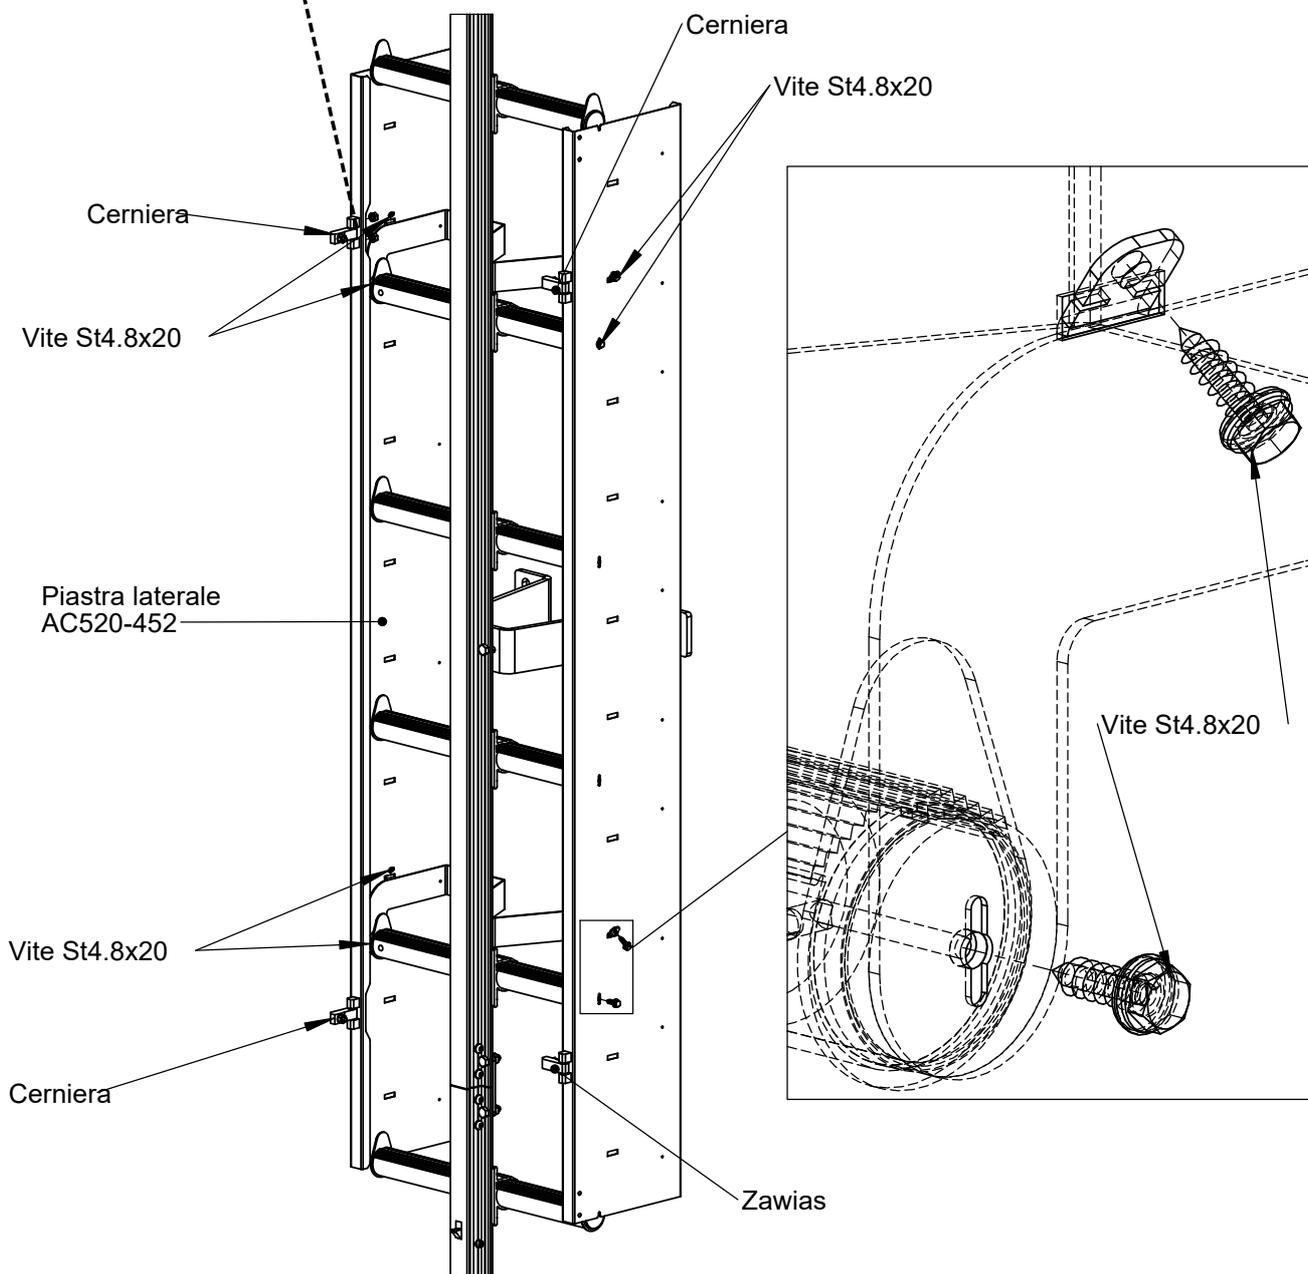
Installazione delle piastre laterali AC520-452 sulle piastre di supporto, mediante quattro viti St4.8x20.
